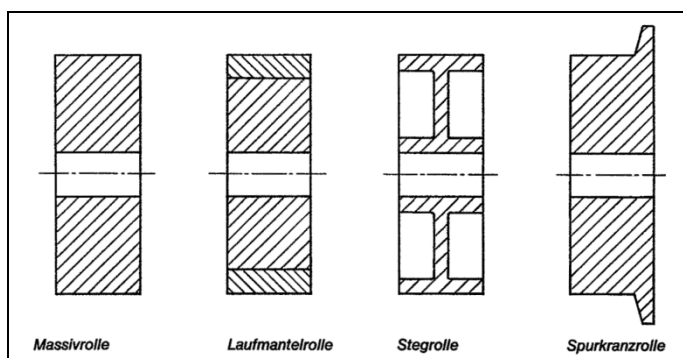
Laufrollen: Grundformen, unterschieden nach Rollenkörper [1]
